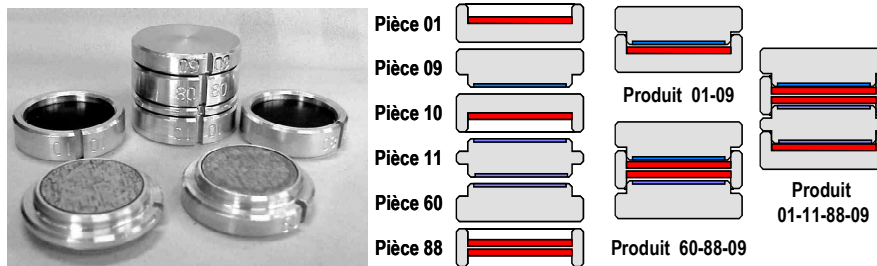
Types de pièces et exemples de produits assemblés sur le SFP
